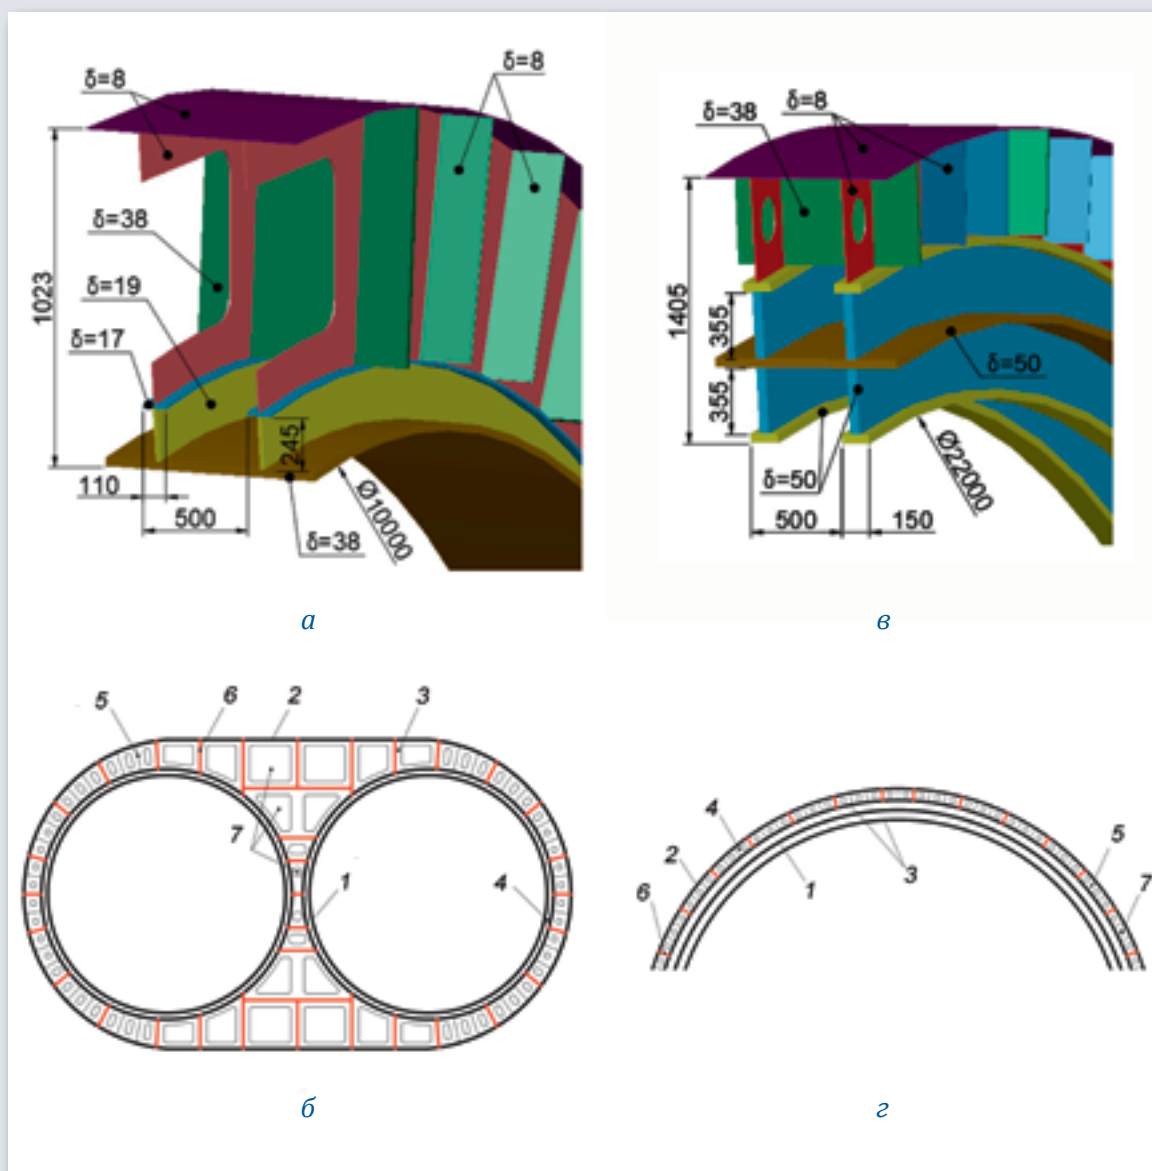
Параметры сечений отсека II (а, б) и отсека VII (в, г): 1 – оболочка прочного корпуса; 2 – оболочка лёгкого корпуса; 3 – шпангоут лёгкого корпуса; 4 – шпангоут прочного корпуса; 5 – стрингер толщиной 8 мм; 6 – стрингер толщиной 38 мм; 7 – вырезы в шпангоуте
